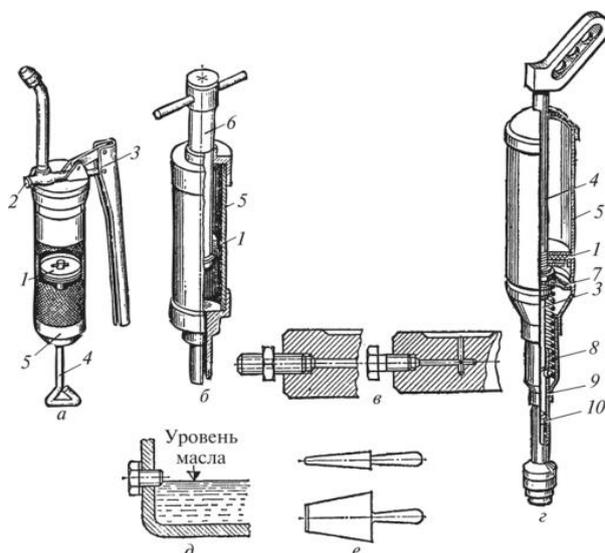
Приборы и приспособления для смазывания механизмов
